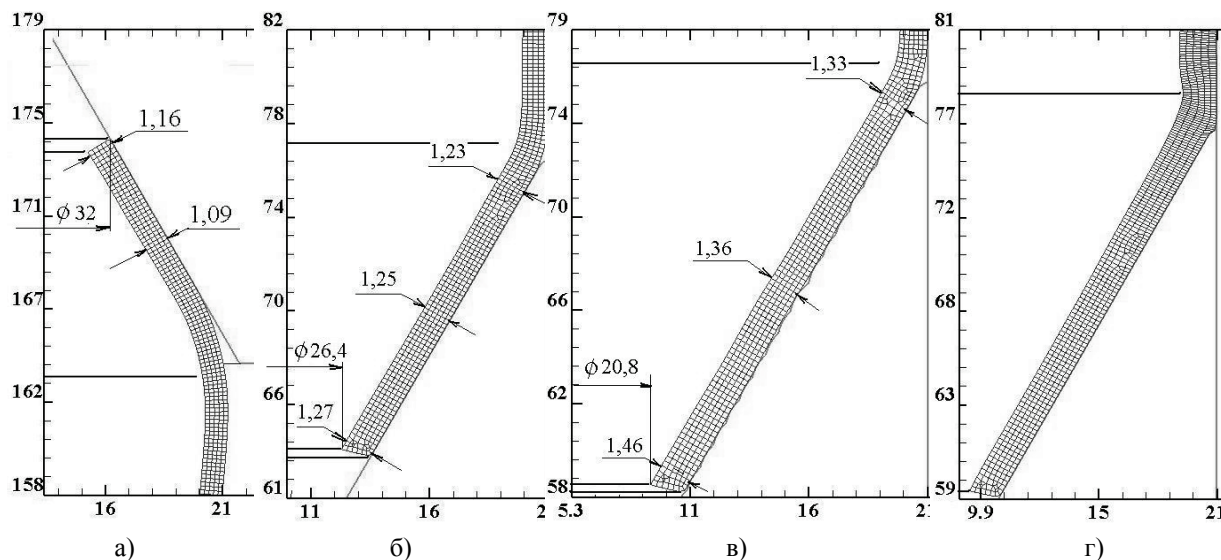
Форма та розміри в міліметрах zdeформованих частин заготовок: а – заготовка після ВО, б – заготовка після ЗО в ТКМ, в і г – заготовки після ЗО КМСП в момент потовщення стінки
